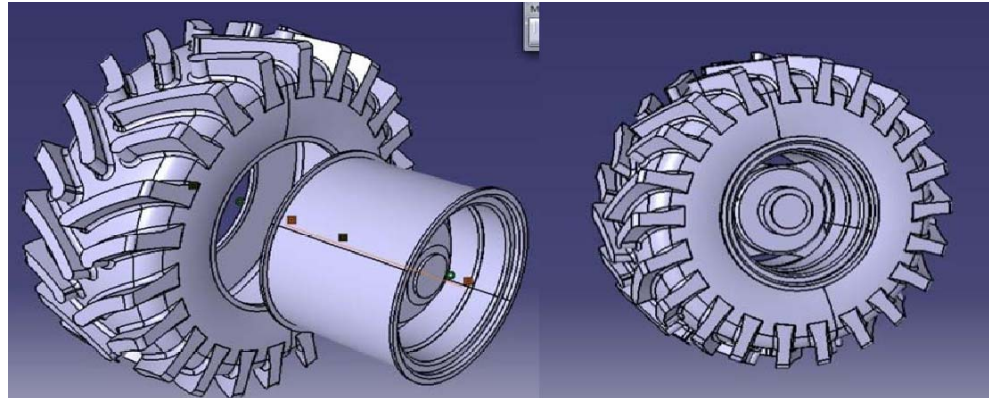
Ensamblaje de ruedas (neumático-llanta).
